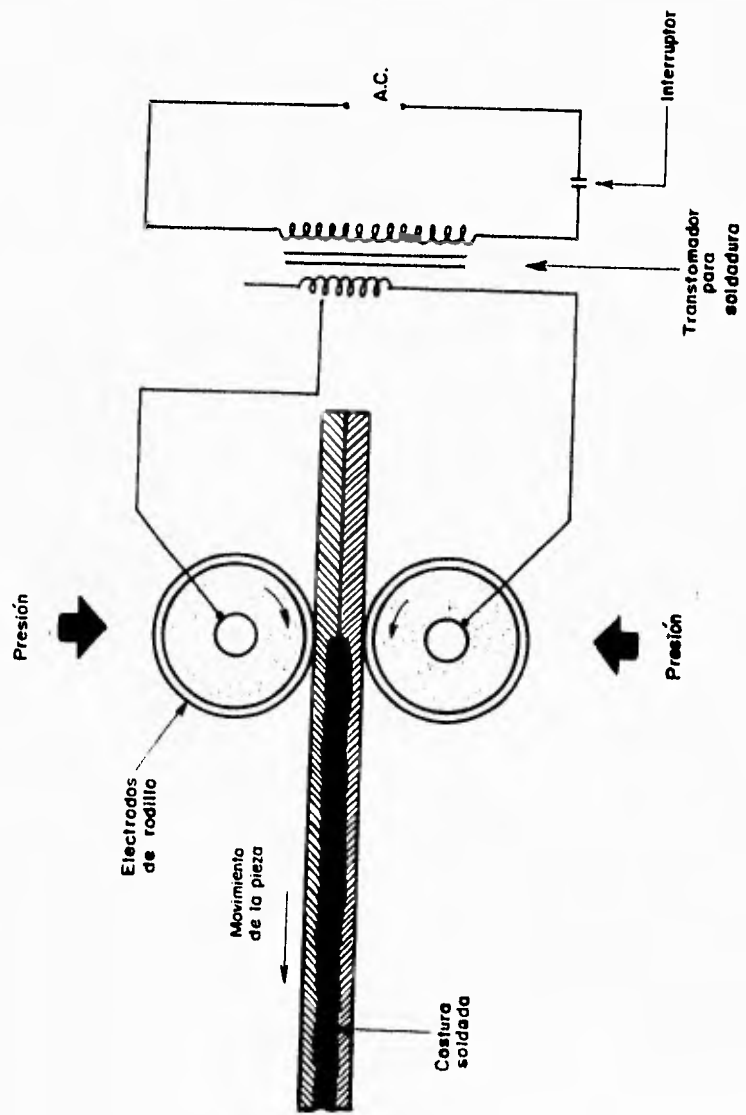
Soldadura por costura (RSEW)
